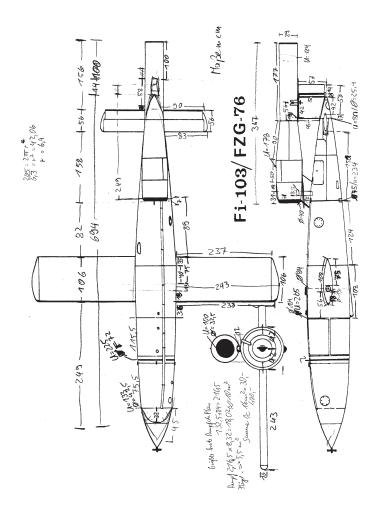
An- und Aufsichtsplan mit eingetragenen Maßen Fig. 95 Inspection plan and blueprints with dimensions, drawing
